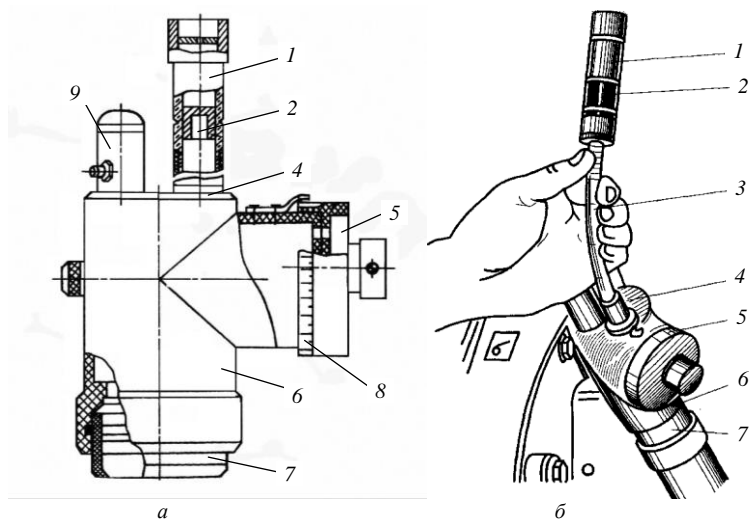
Устройство индикатора КИ-13671 (а) и измерение расхода картерных газов индикатором КИ-13671 (б): 1 – сигнализатор; 2 – поршень сигнализатора; 3 – удлинитель; 4 – патрубкок; 5 – крышка; 6 – корпус; 7 – переходник; 8 – шкала; 9 – колпачок
